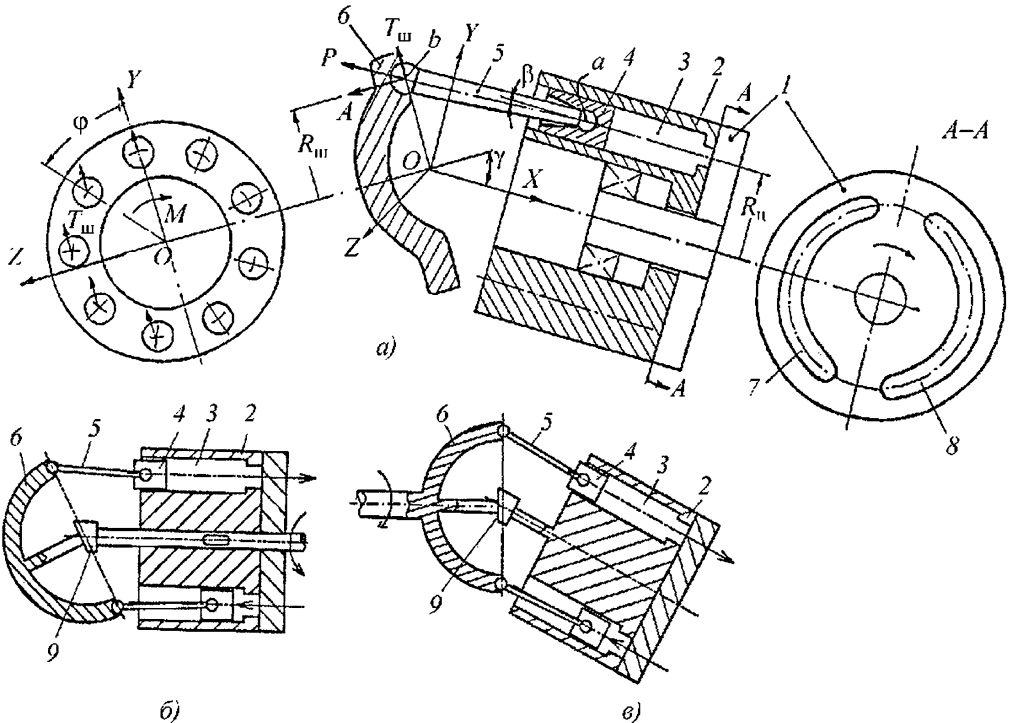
Схемы аксиально-поршневых гидромашин с рычажным механизмом:
